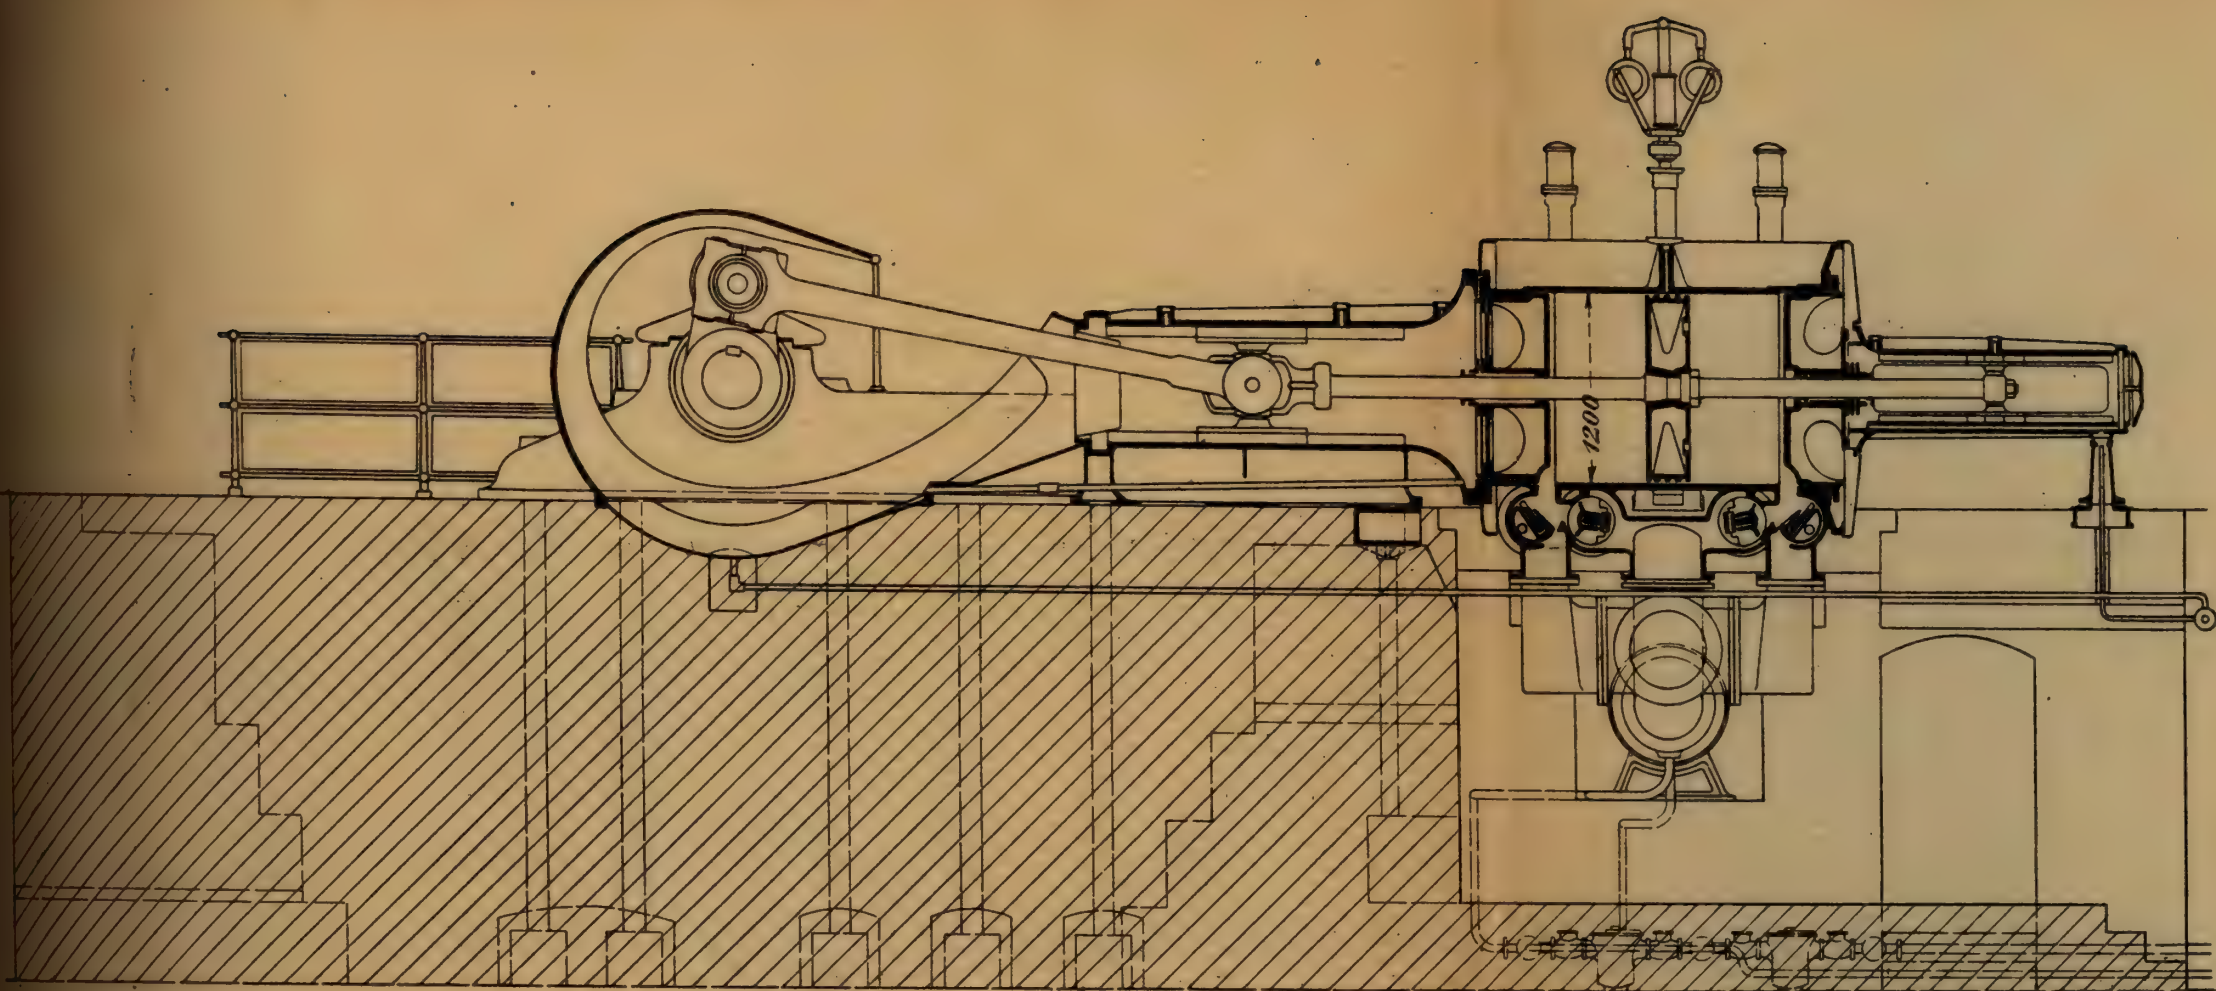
Längsschnitt durch den Niederdruckzylinder.
